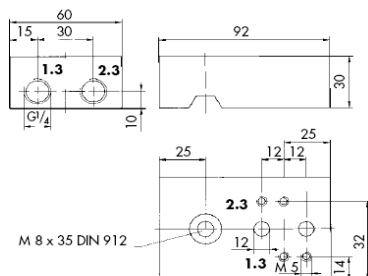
· Plaque d'adaptation profil NAMUR (dimensions en mm)
